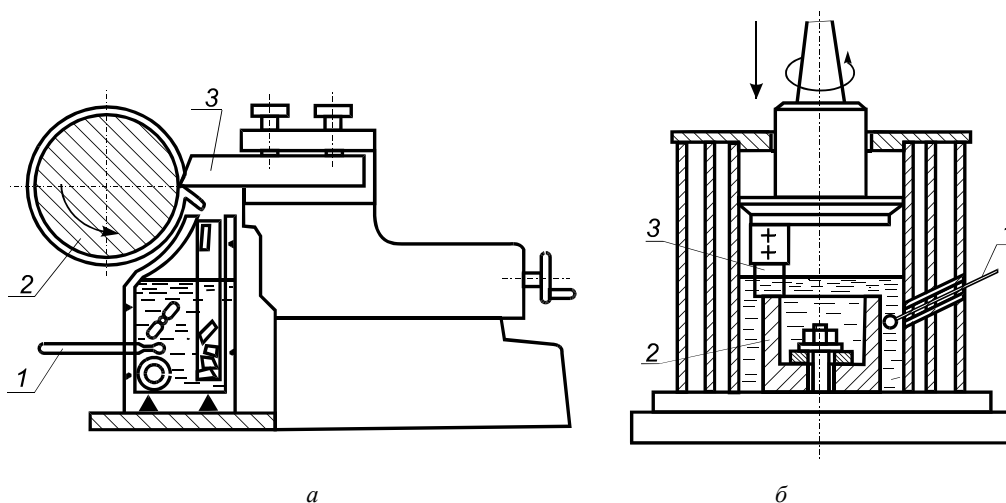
Схемы калориметров: 1 – термометр, 2 – заготовка, 3 – резец
